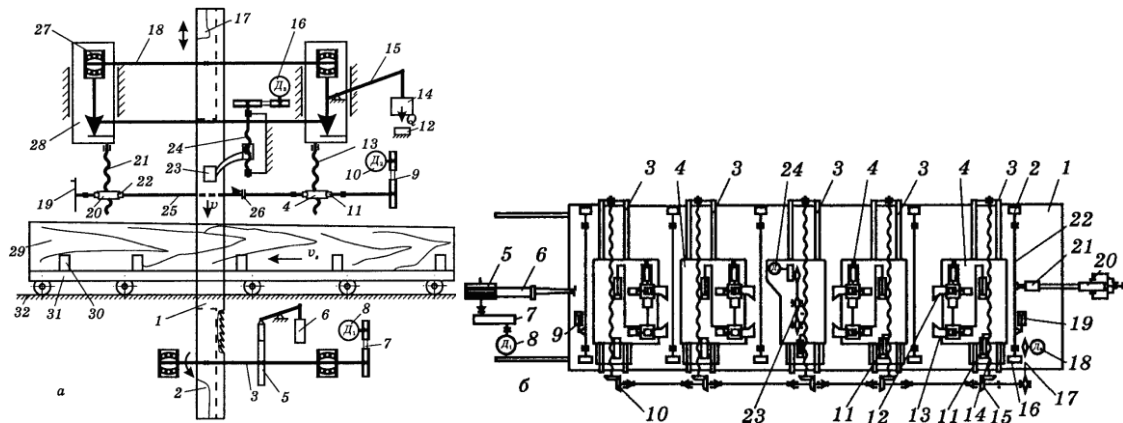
Кінематичні схеми вертикального стрікопильного верстата: *а* – механізму різання: 1 – стрічкова пилка; 2 – приводний шків; 3, 18, 25 – вал; 4, 20 – черв'ячна гайка-шестірня; 5 – стрічкове гальмо; 6 – гідроциліндр; 7 – клинопасова передача; 8, 10, 16 – електродвигуни; 11, 22 – черв'як; 12 – обмежувач; 13, 21, 24 – гвинти; 14 – вага; 15 – важелі; 17 – натяжний шків; 19 – маховичок; 23 – верхня рухома напрямна; 26 – зубчаста муфта; 27 – підшипникова опора; 28 – супорт; 29 – колода; 30 – затискачі; 31 – візок; 32 – рейковий шлях; *б* – механізму подачі: 1 – платформа; 2, 16 – колесо; 3 – напрямна; 4 – стійка; 5, 6, 7, 8, 20, 21 – ланцюговий привод; 9, 19 – гідроциліндри; 10, 15 – конічні передачі; 11 – додатковий гідроциліндр; 12, 13 – затискач; 14 – гвинт; 17 – ланцюгова передача; 18 – електродвигун; 22 – вісь; 23 – механізм повороту колоди; 24 – привод
